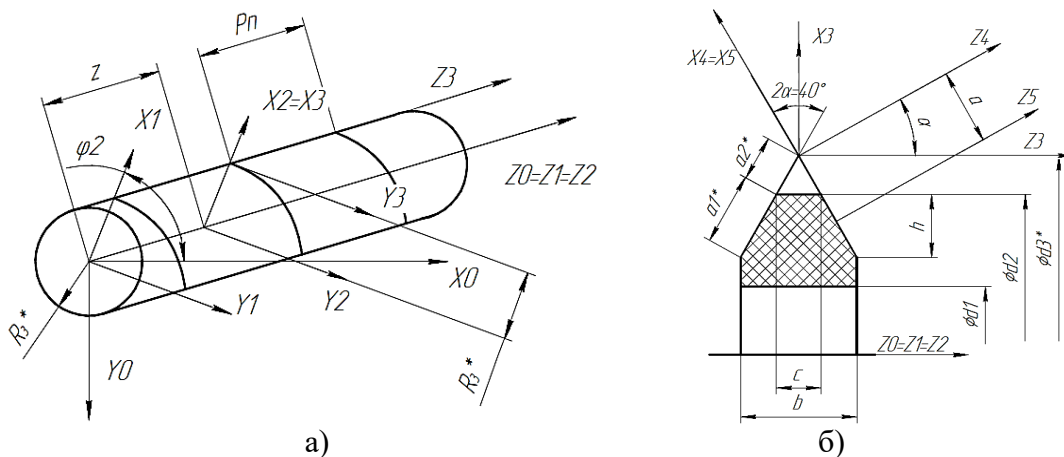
Схема взаємодії оброблюваної деталі і інструмента: а) вид зверху та б) вид збоку
